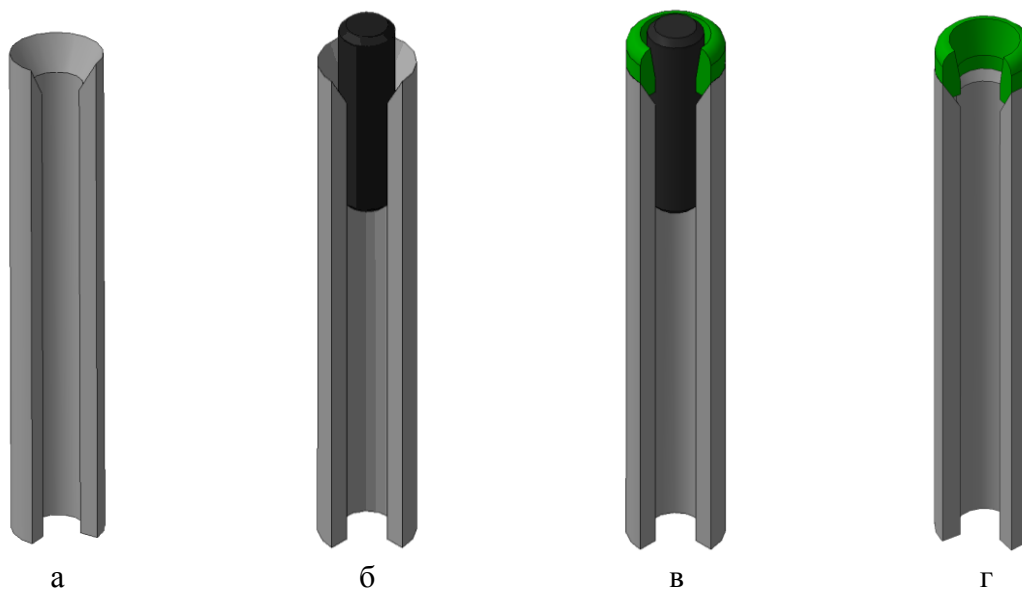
Последовательность изготовления износостойкого патрубка с применением наплавки: а – заготовка; б – заготовка перед наплавкой с установленным формирующим элементом; в – наплавленный патрубок; г – патрубок с удаленным формирующим элементом
